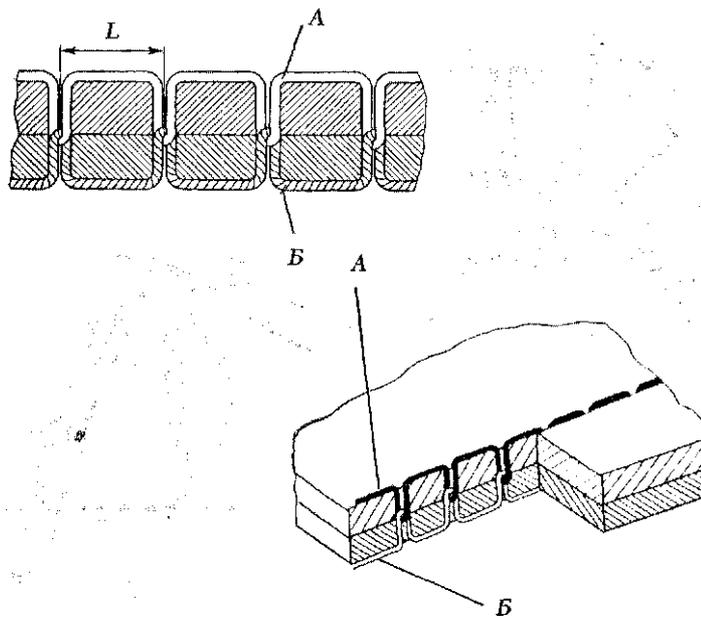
, 2. Зовнішній вигляд човникового стібка: А — голкова нитка (верхня нитка); Б — човникова нитка (нижня нитка)
